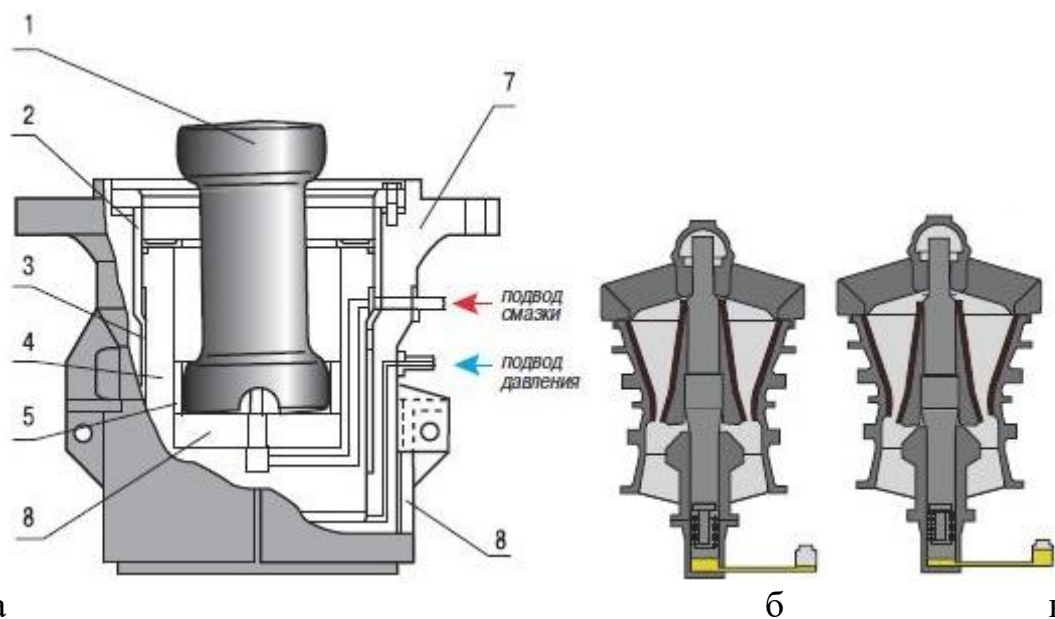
Общий вид инерционной дробилки системы Механобр: 1 – опорный вал; 2 – втулка; 3 – уплотнение; 4 – плунжер; 5 – втулка; 6 – подпятник; 7 – корпус гидроцилиндра; 8 – броня; б – дробящий конус поднимается при нагнетании масла в гидроцилиндр; в – дробящий конус опускается при сливе масла из гидроцилиндра в бак
